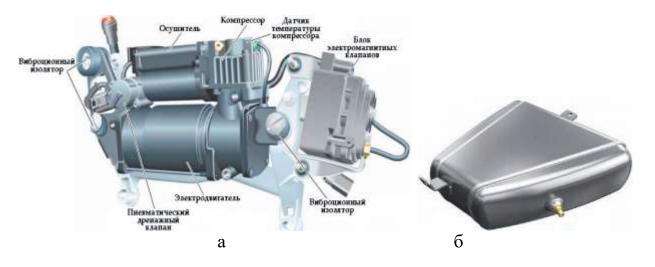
Компоненты пневмосистемы: а – модуль подачи воздуха; б – ресивер
